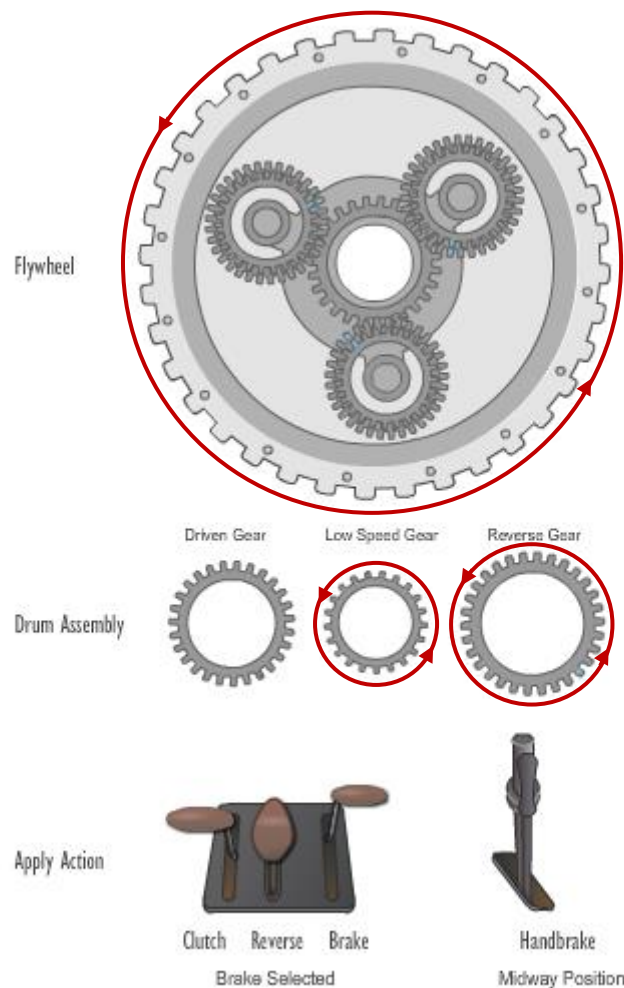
Movimiento de los engranajes y posición de los pedales al accionar el freno [6]
